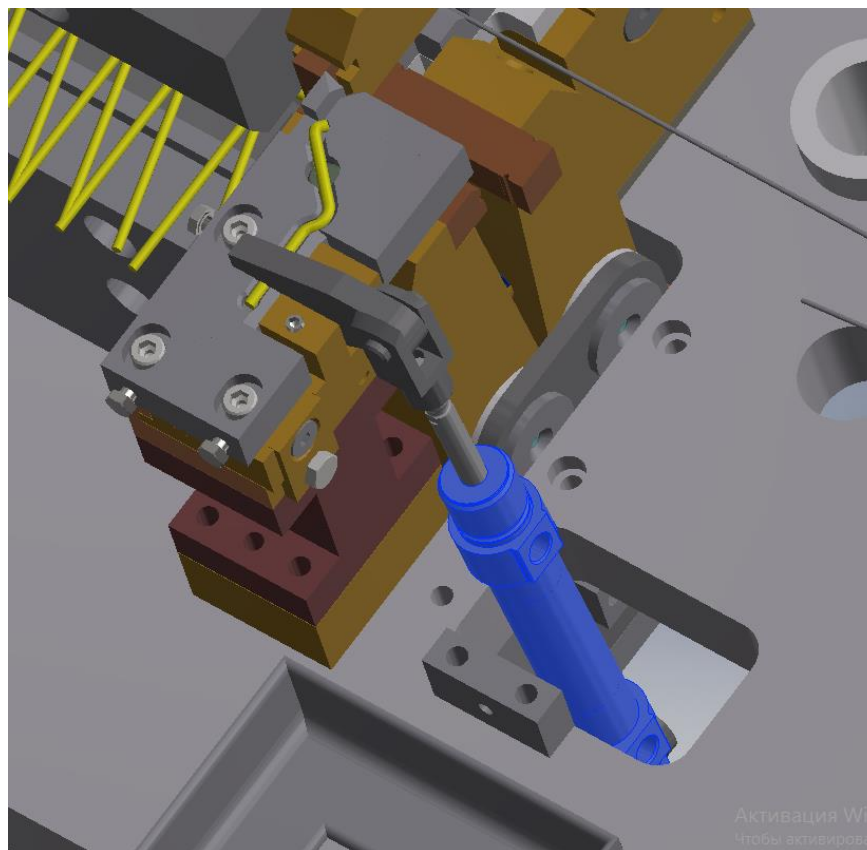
Пневматичний циліндр фірми FESTO у робочому положенні
